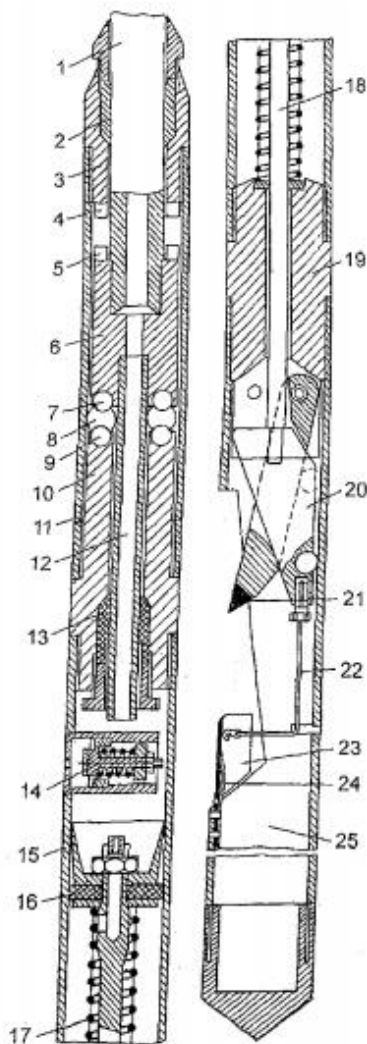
Схема однорезцового пробоотборника вибрационного типа конструкции И.Б.Булнаева:
